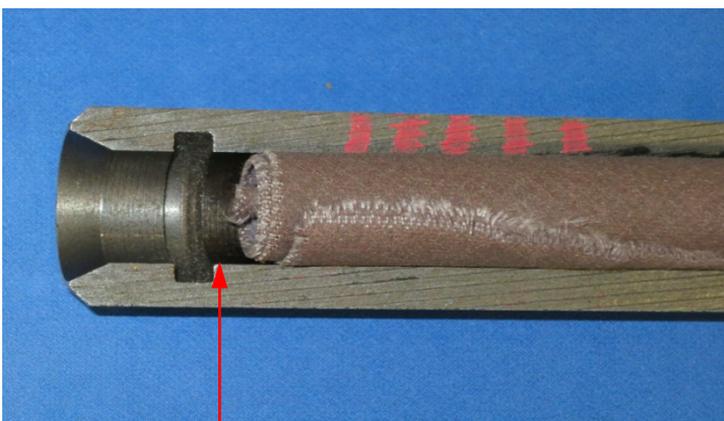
Werkzeug stoppt vor der Nut des O-Rings
